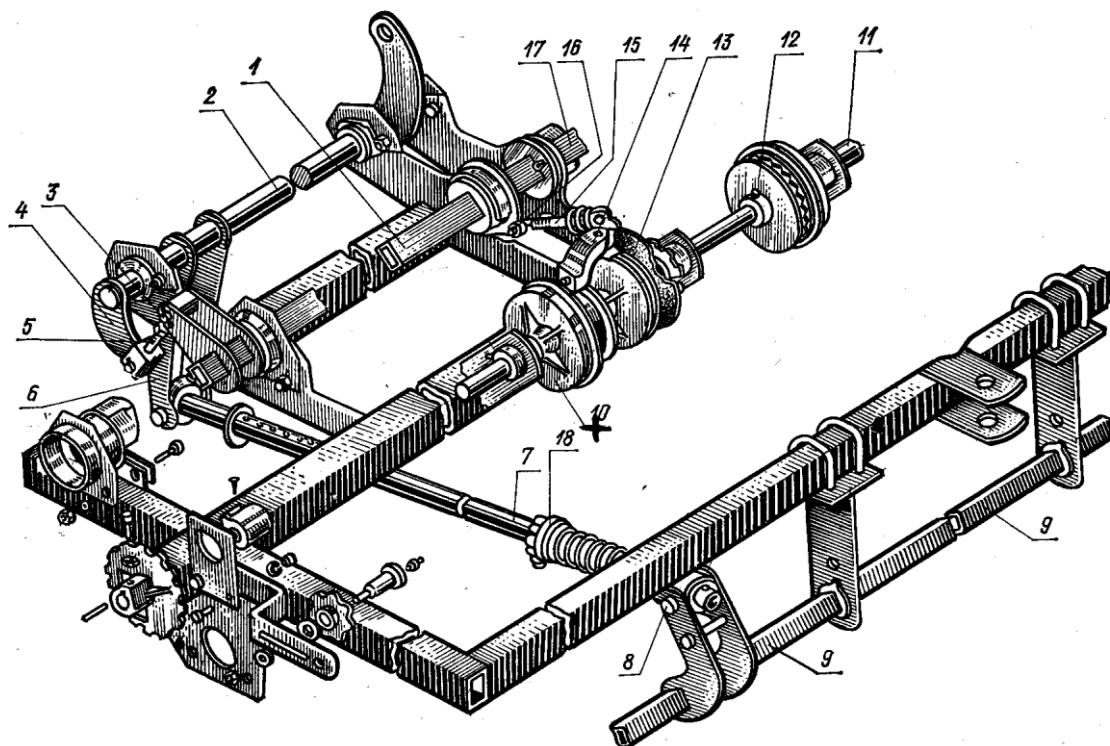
Валы подъема сошников, контрпривод, валы загортачей
